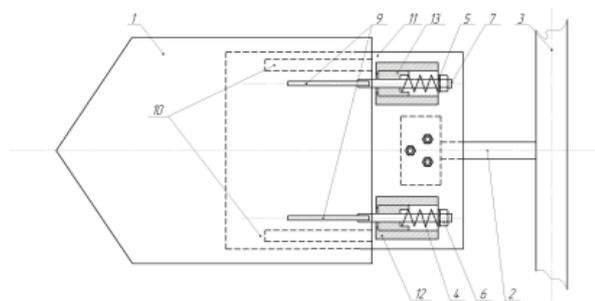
Конструктивно-технологическая схема приемного лемеха для подкапывания/подбора корнеплодов и луковиц: 1 – лемех; 2 – пружина; 3 – рама; 4 – опорный упругий элемент; 5 – шайба; 6 – гайка; 7 – шток; 8, 9 – толкатели; 10 – направляющие; 11 – плита опорная; 12 – втулка
